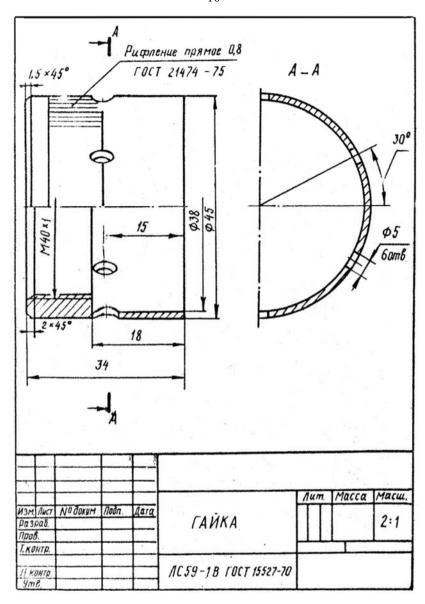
Рабочий чертеж гайки (деталь поз. 7)
